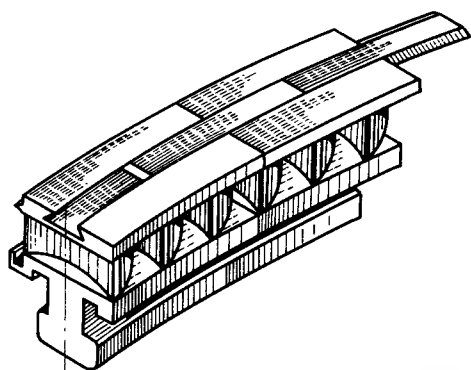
Пакеты рабочих лопаток с демпферной связью регулирующей ступени ЦВД
